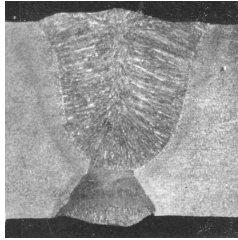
Макроструктура сварного шва, выполненного электродуговой сваркой
